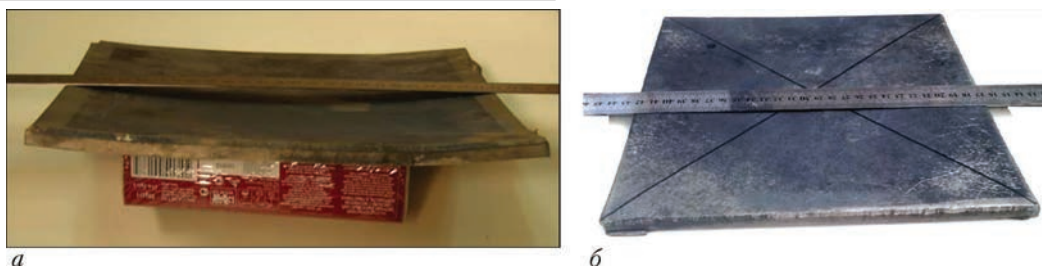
Внешний вид сваренной взрывом заготовки: а — до правки, б — после
